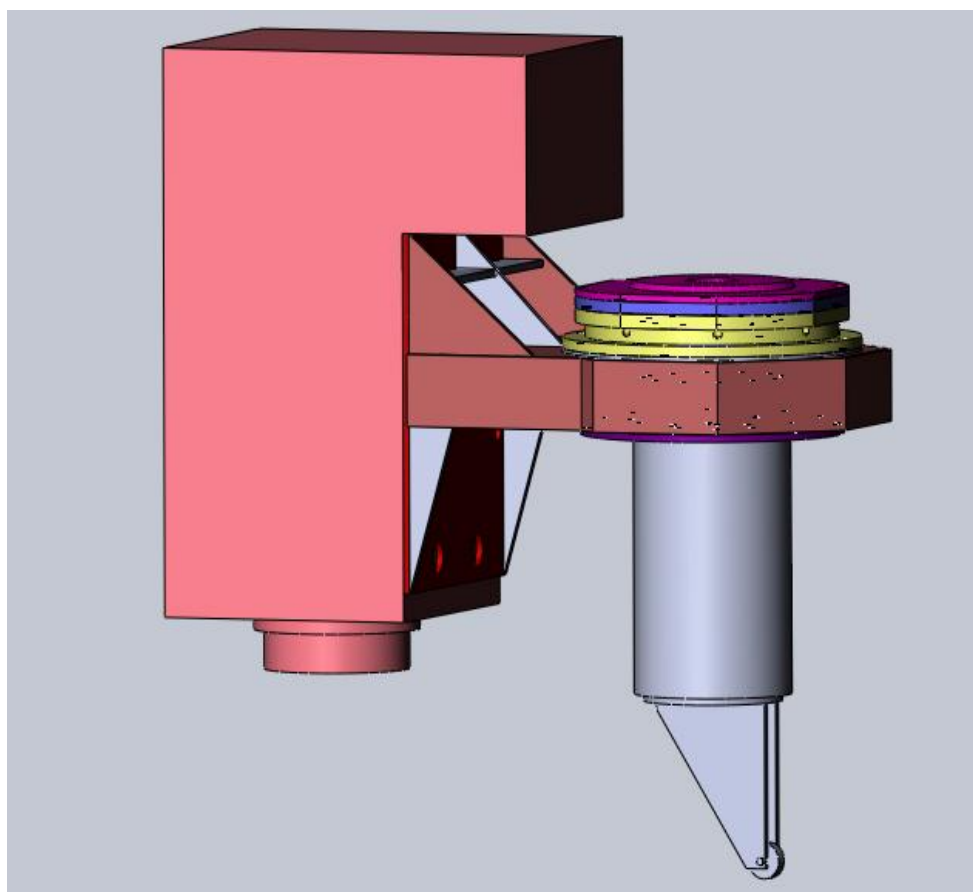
Вариант компоновки для накатки внутренней криволинейной поверхности кристаллизаторов
